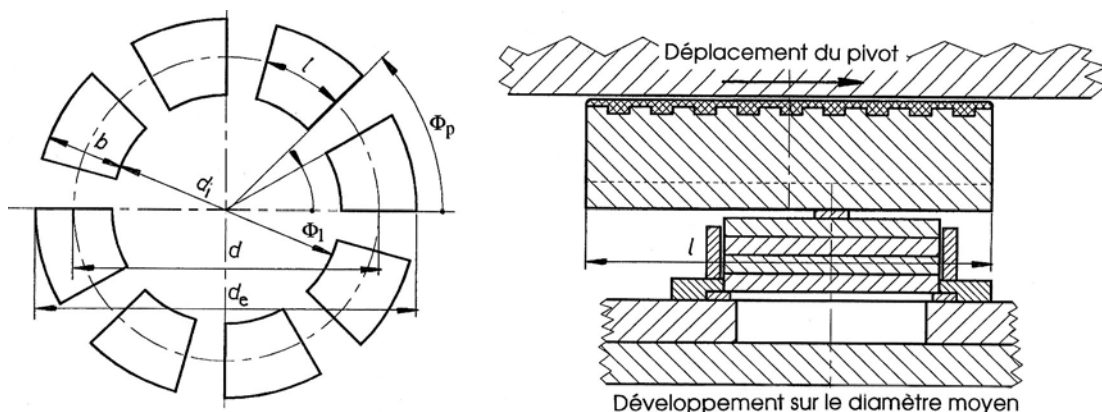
Dimensions générales de la butée ou guidage hydrodynamique à patins
